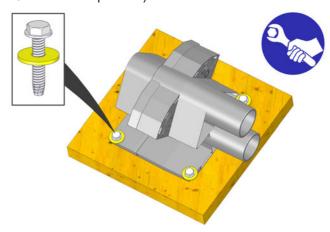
Sonde d'aspiration sur une planche de bois
